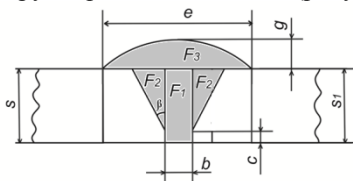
Схема сварного соединения труб типа С17
